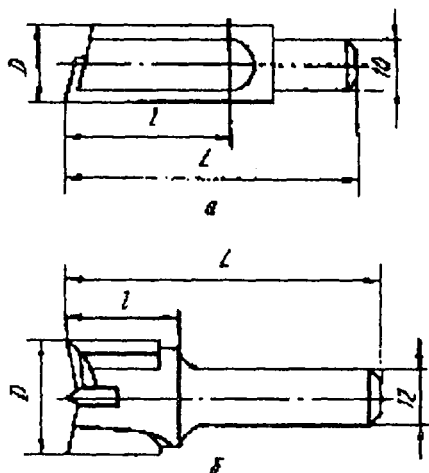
Фрезы концевые цилиндрические с твердосплавными пластинами:
